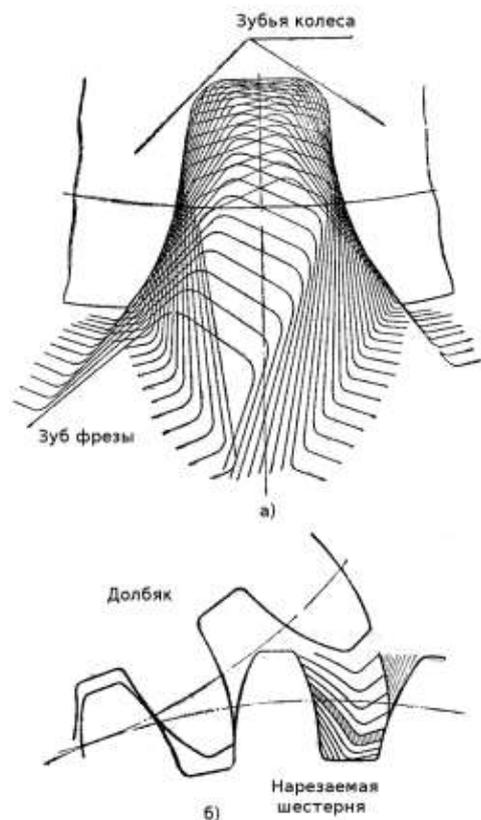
Образование эвольвентного профиля: а — червячной фрезой; б — зуборезным долбяком.
